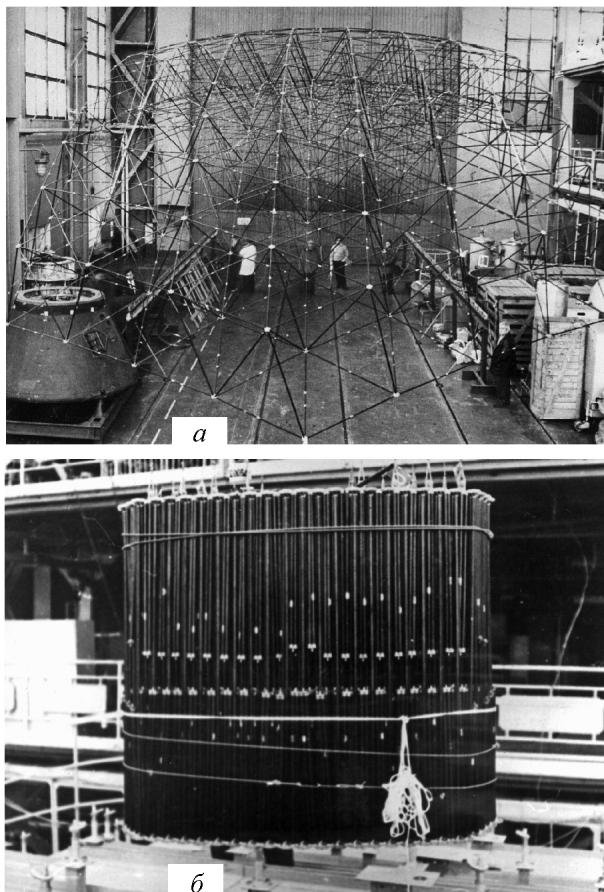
Раскрывающийся крупногабаритный рефлектор ферменного типа:
